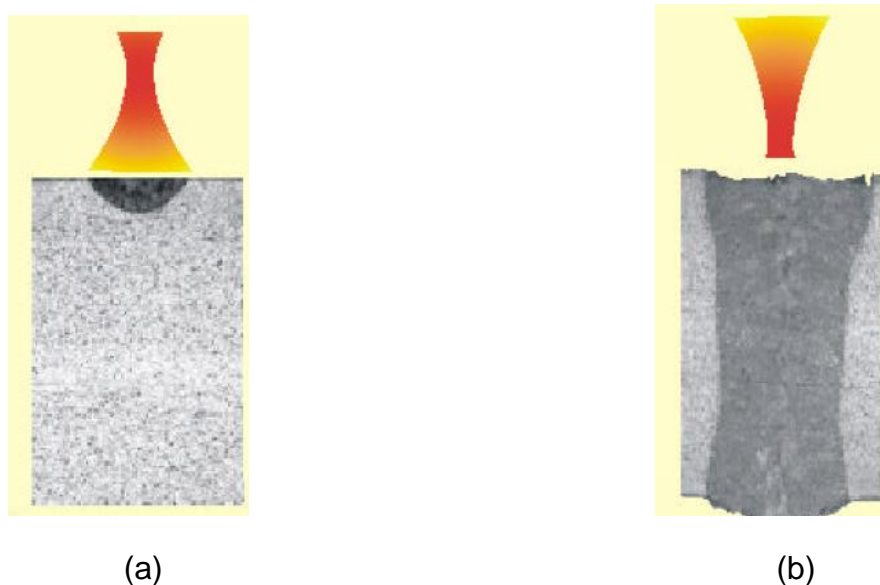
As técnicas de soldagem a laser: (a) condução, (b) penetração
